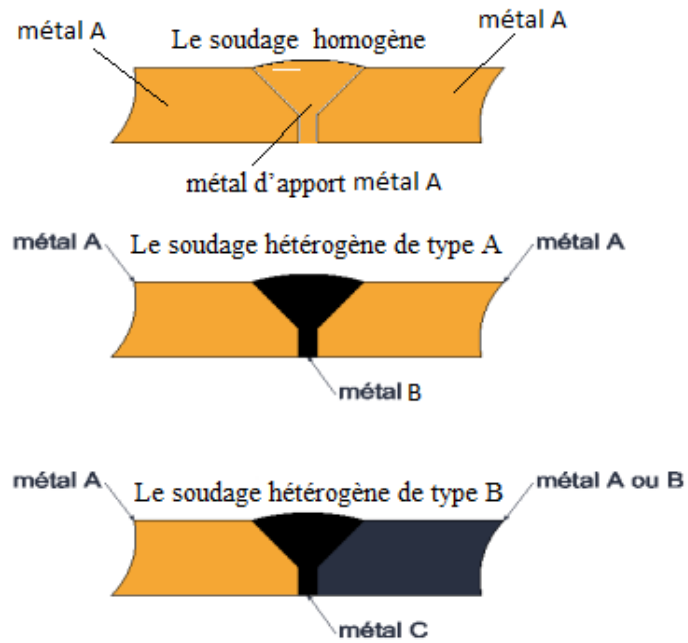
Assemblage de deux pièces par soudage [4].
